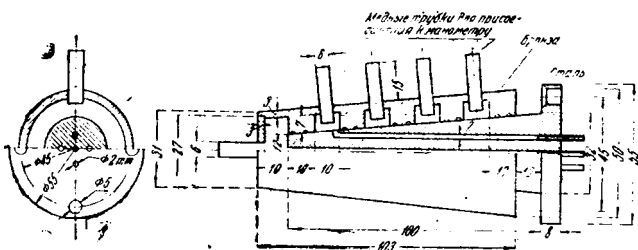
Соединительный пятиходовый конус—приспособление для измерения давлений в каналах ротора
